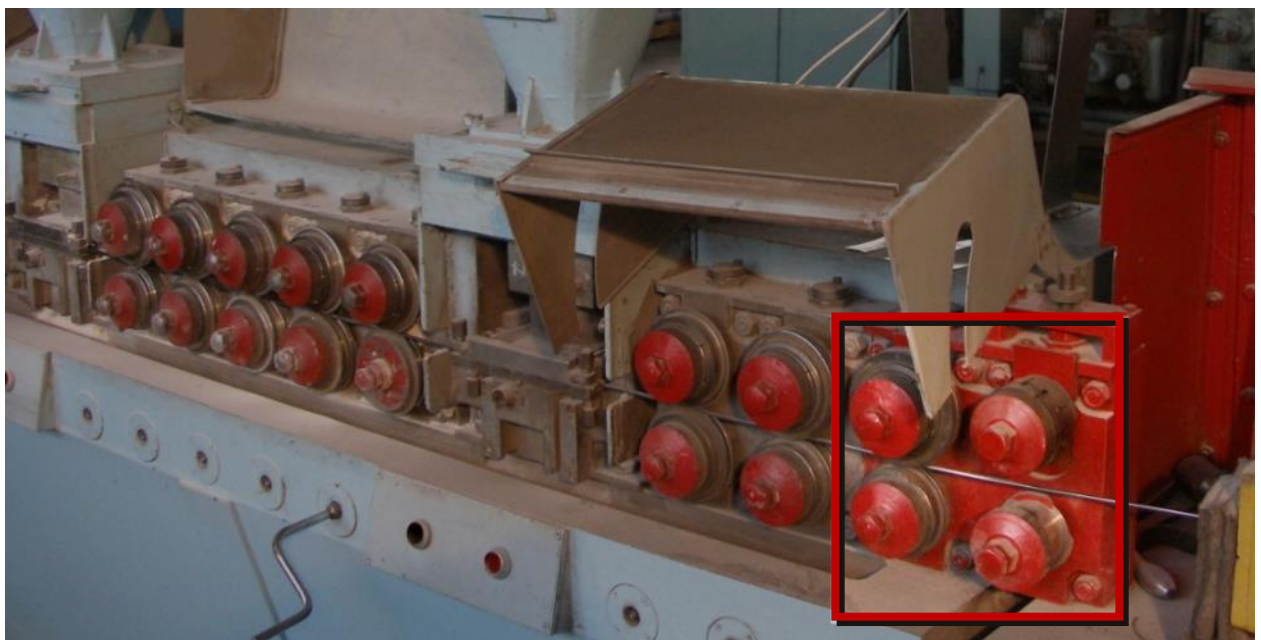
Два додаткові блоки роликового редукування заготовки порошкового дроту, встановлені на агрегаті формовки.
